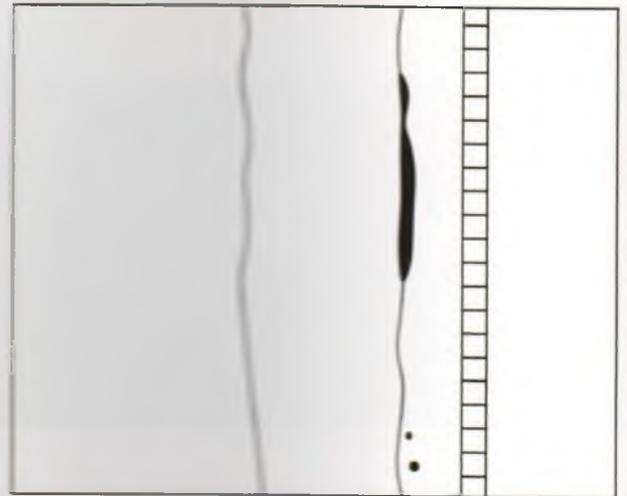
Результат процесса ножевой коррозии – сквозные коррозионные разрушения – в зоне сплавления сварного соединения на внутренней поверхности стенки бака-аккумулятора для хранения горячей воды
